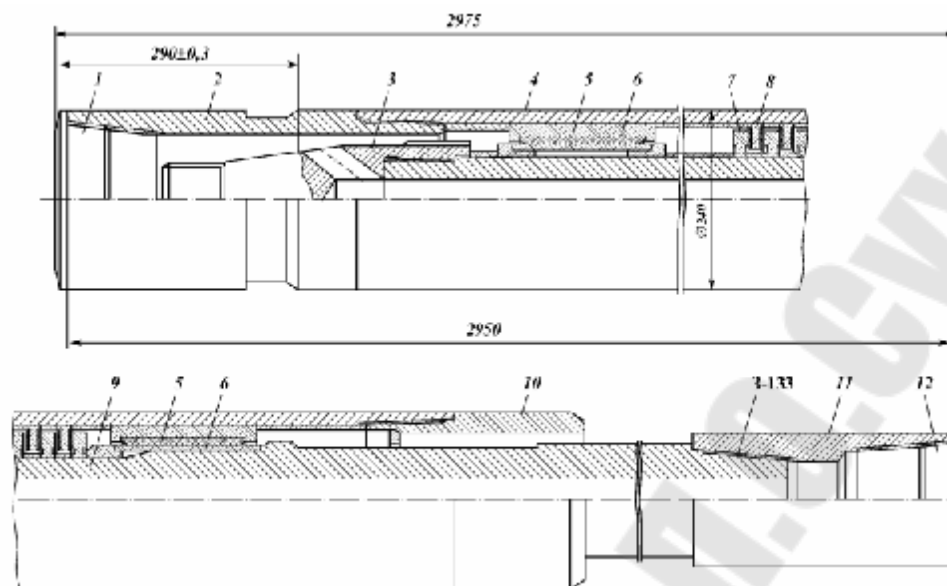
Конструкция шпинделя ШП-240: 1 – пробка верхняя; 2 – переводник верхний; 3 – полумуфта; 4 – корпус; 5 – опора радиальная; 6 – втулка радиальной опоры; 7 – диск пяты; 8 – подпятник; 9 – вал; 10 – ниппель; 11 – переводник наддолотный; 12 – пробка нижняя
